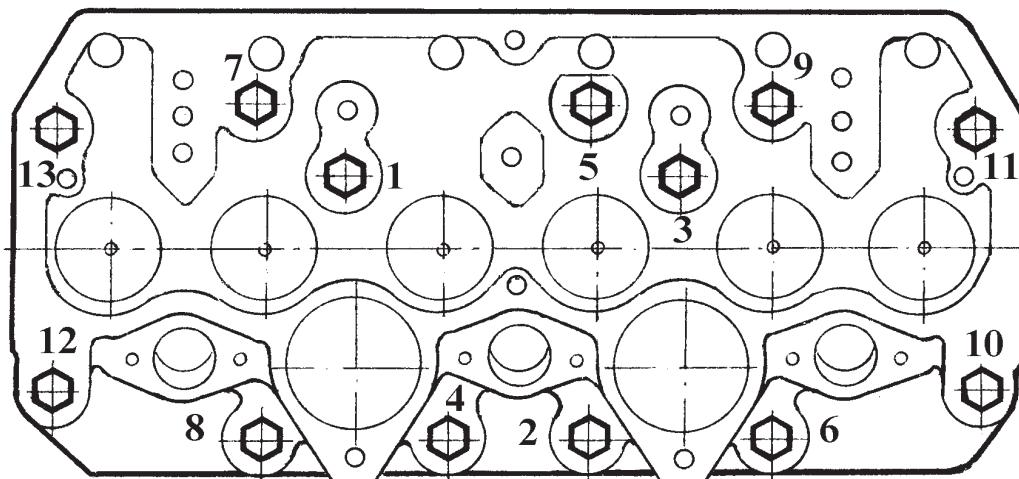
Схема последовательности затяжки болтов крепления головки цилиндров
